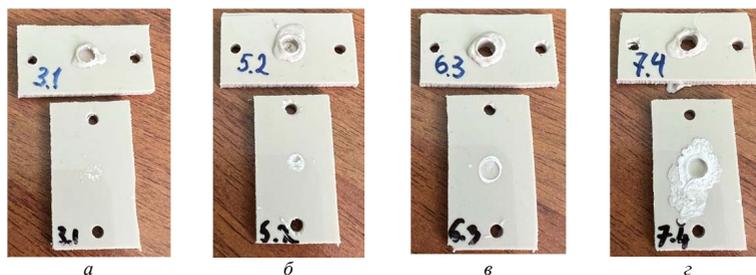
Внешний вид поверхностей разрыва сварного соединения
